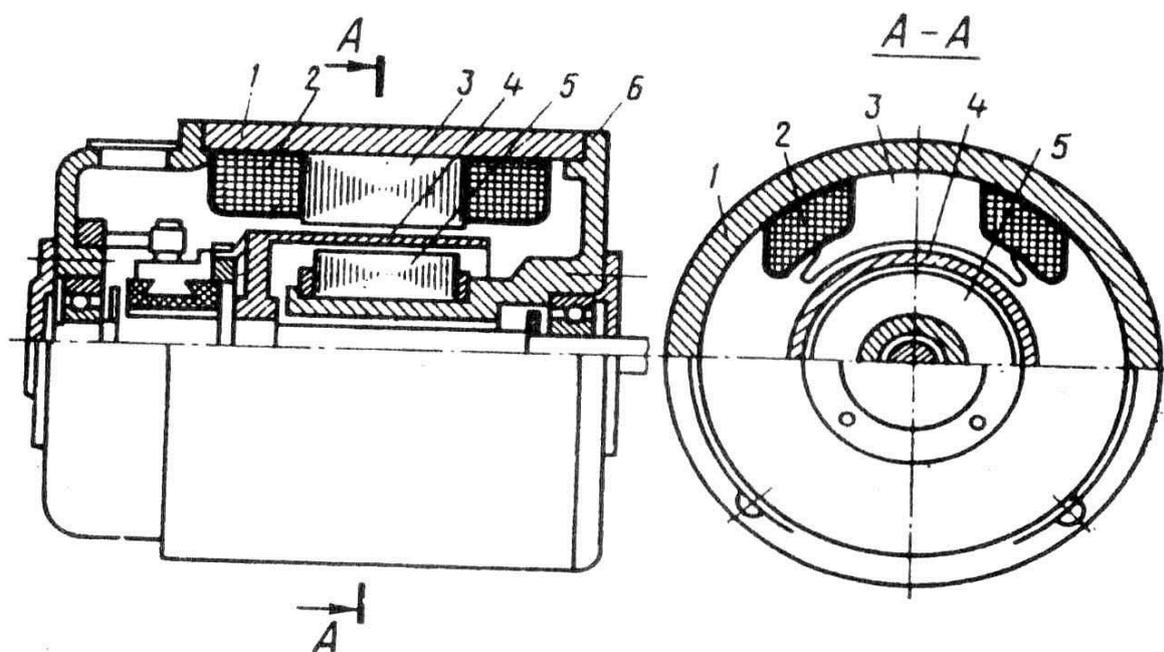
Малоинерционный исполнительный двигатель постоянного тока с полым якорем:
